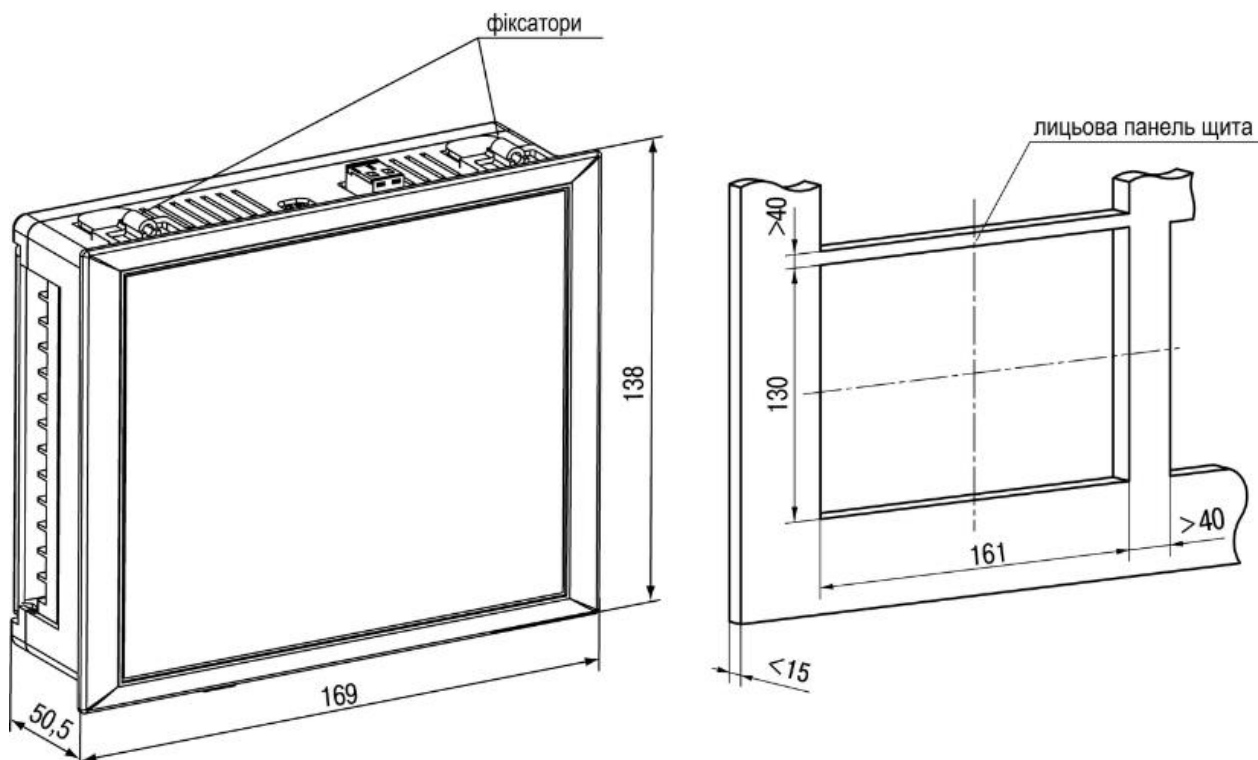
Габаритні розміри корпусу Щ7
